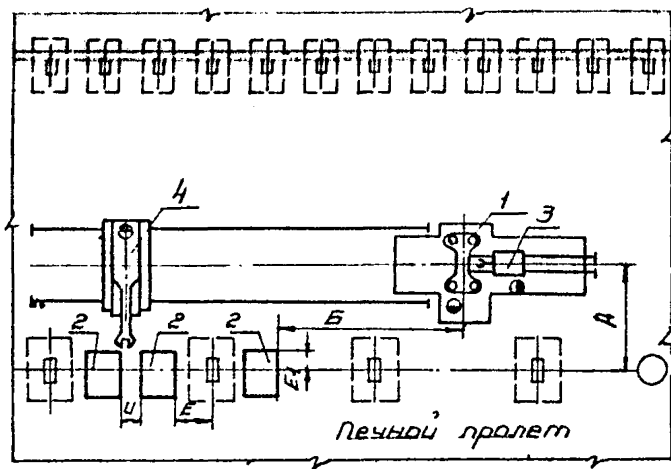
Схема расположения участка гидравлических ковочных прессов усилием 8000-12500 кН:
